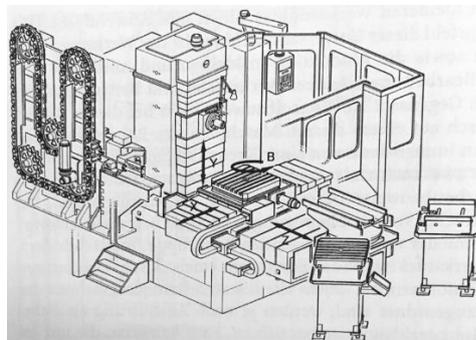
Universalfräsmaschine (horizontale Werkzeugspindel)
